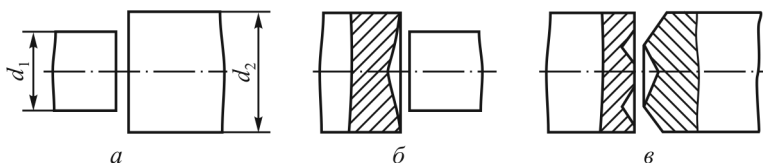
Подготовка контактных поверхностей заготовок из разнородных материалов к сварке: *а* – быстрорежущая сталь – конструкционная сталь; *б* – коррозионностойкая сталь – алюминий; *в* – коррозионностойкая сталь – цинк;  $d_2 = (1,15...1,25) d_1$
